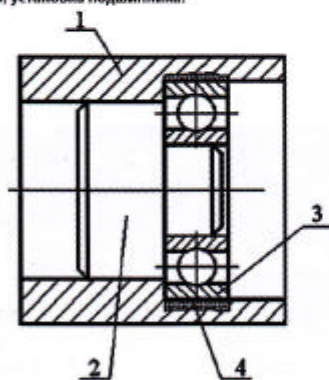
Восстановление опорной поверхности подшипника с использованием специального центрирующего приспособления
